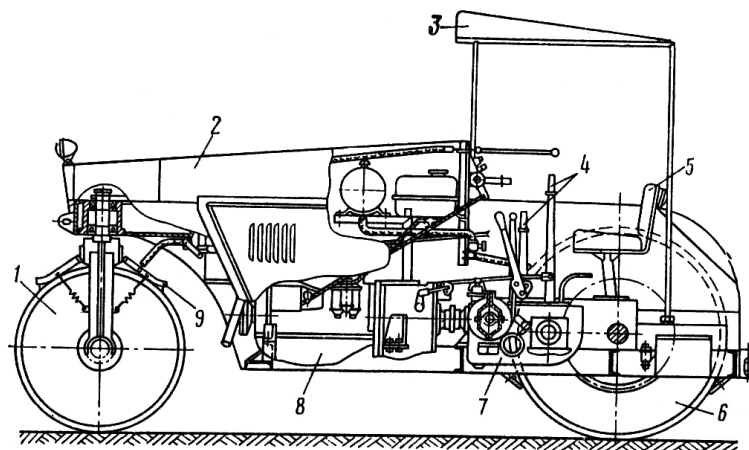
Схема самоходного катка с гладкими вальцами ДУ-50: 1 – передний управляемый валец; 2 – корпус; 3 – тент; 4 – рычаги управления; 5 – сиденье; 6 – ведущие вальцы; 7 – коробка передач; 8 – двигатель; 9 – устройство для очистки и смачивания вальца
